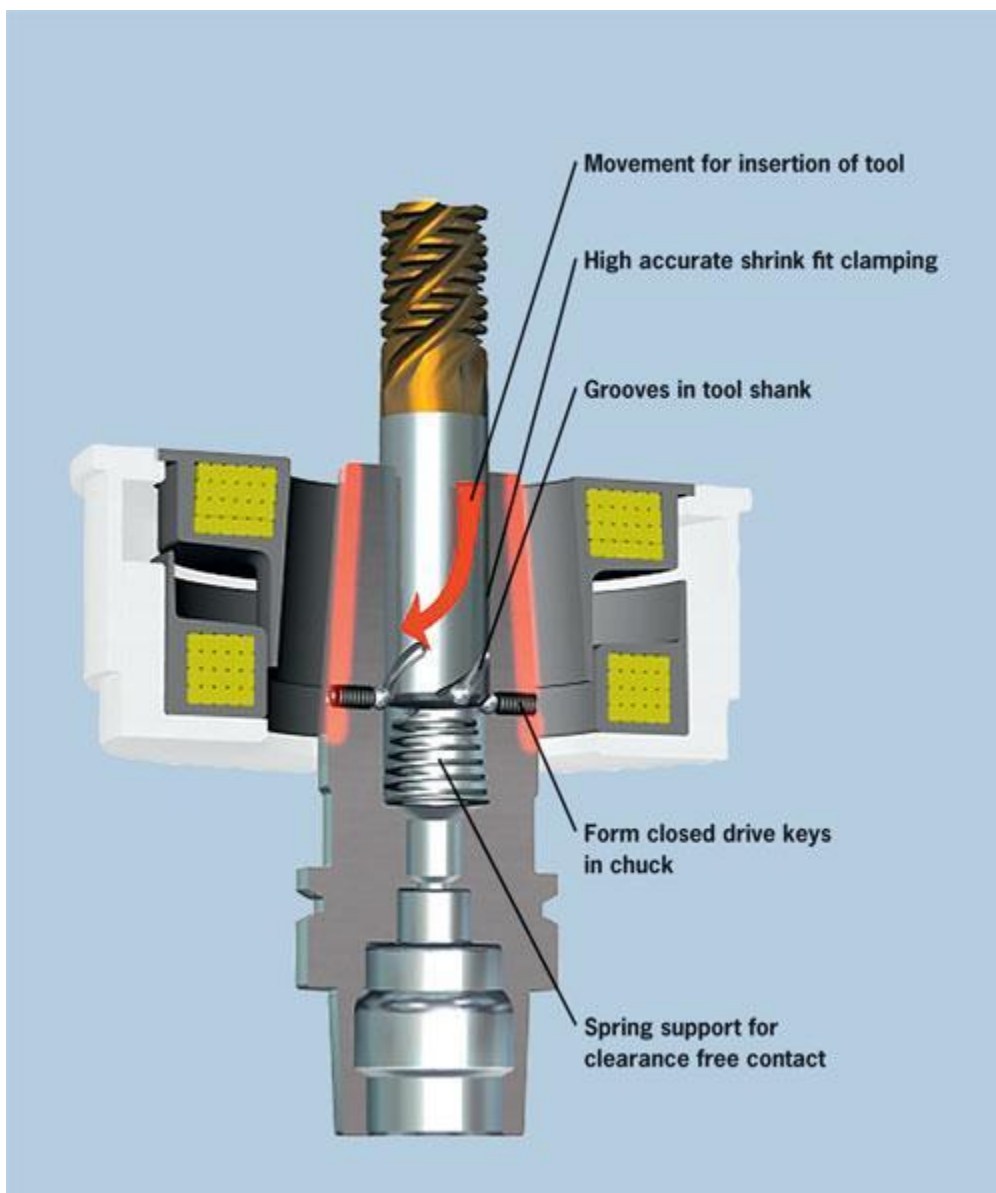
Příklad upínače a nástroje se systémem Safelock[45]
